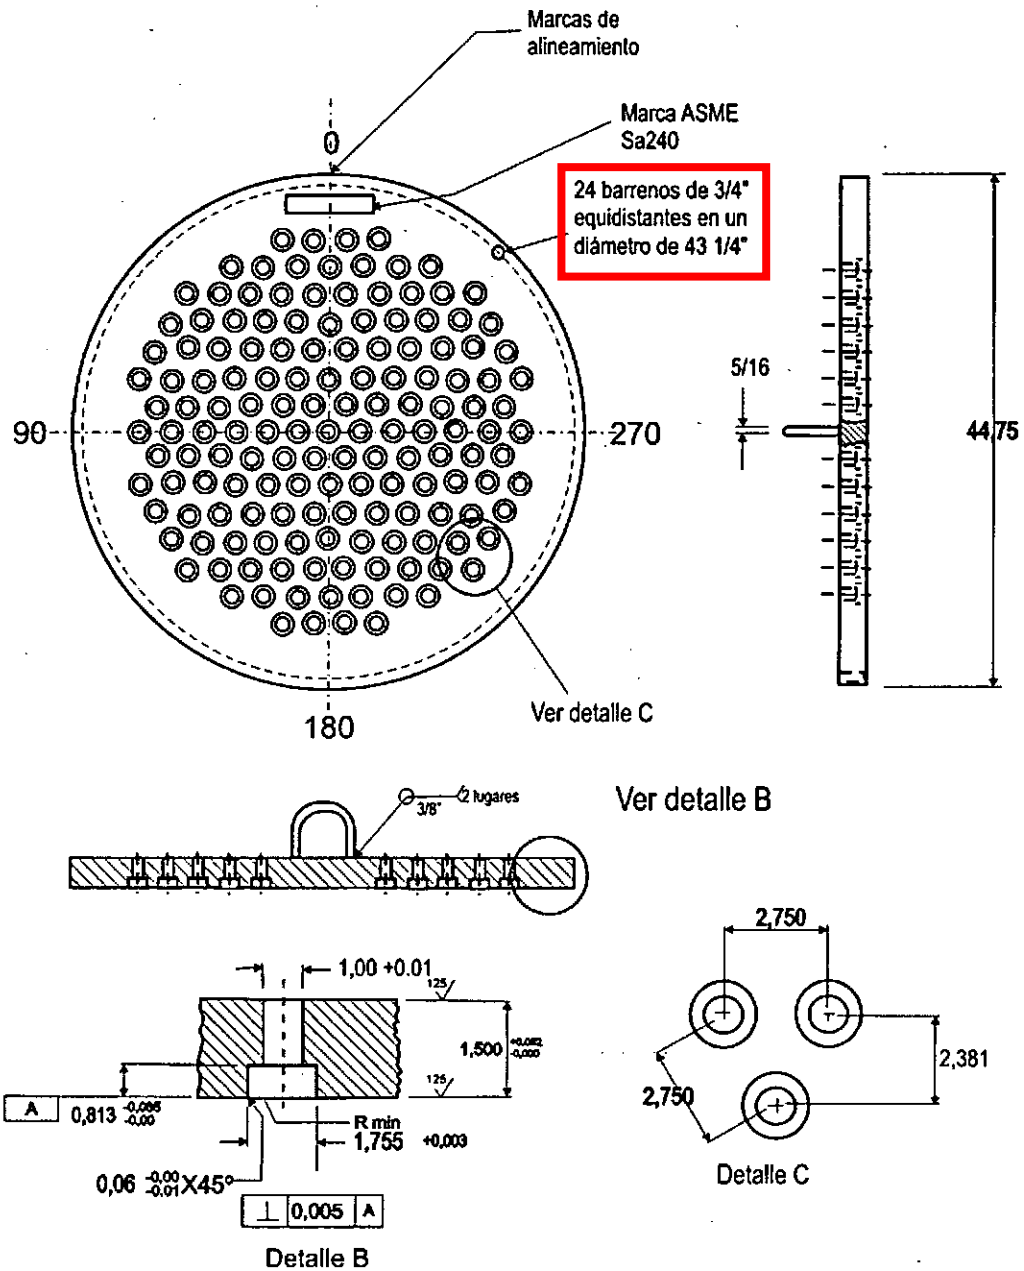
VISTA DE PLANTA DEL ESPEJO.
